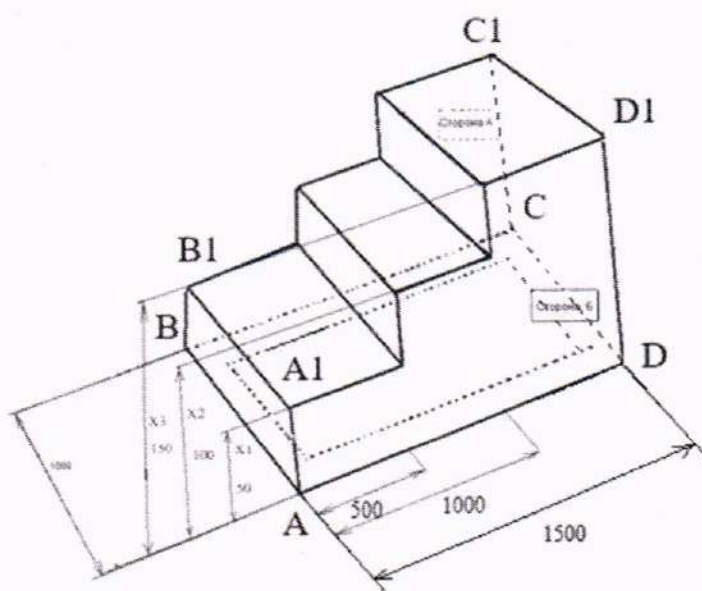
Общий вид имитатора для поверки модулей ЛКПС ТРМЕ.441589.080
